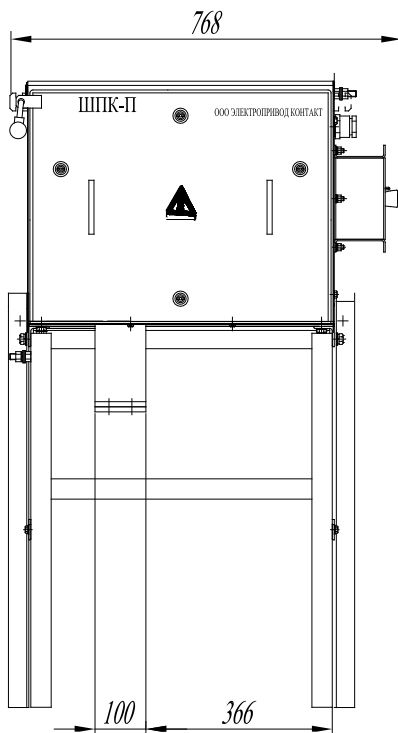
Шкаф ШПК. Габаритные, установочные и присоединительные размеры
